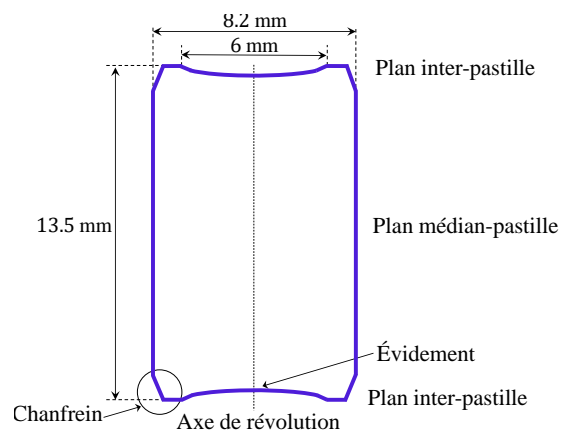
Dimensions d'une pastille de combustible d'un REP 900 MWe
